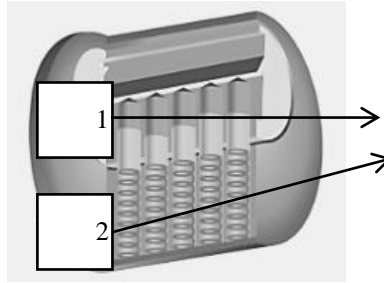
Загальний вигляд циліндрового механізму (вид в розрізі)
